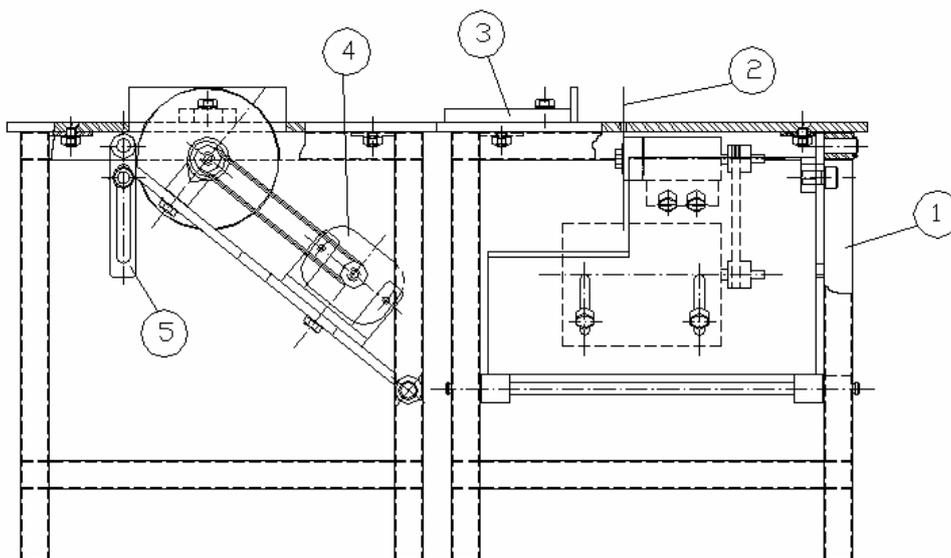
Desenho de Conjunto da Máquina de Corte: 1) estrutura da máquina, 2) disco de corte, 3) dispositivo de regulagem da largura de corte, 4) motor elétrico, 5) dispositivo de regulagem da altura de corte.
